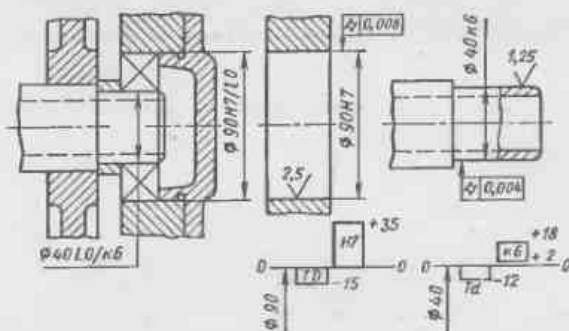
Обозначение посадок подшипников качения на сборочных чертежах и полей допусков на чертежах деталей
